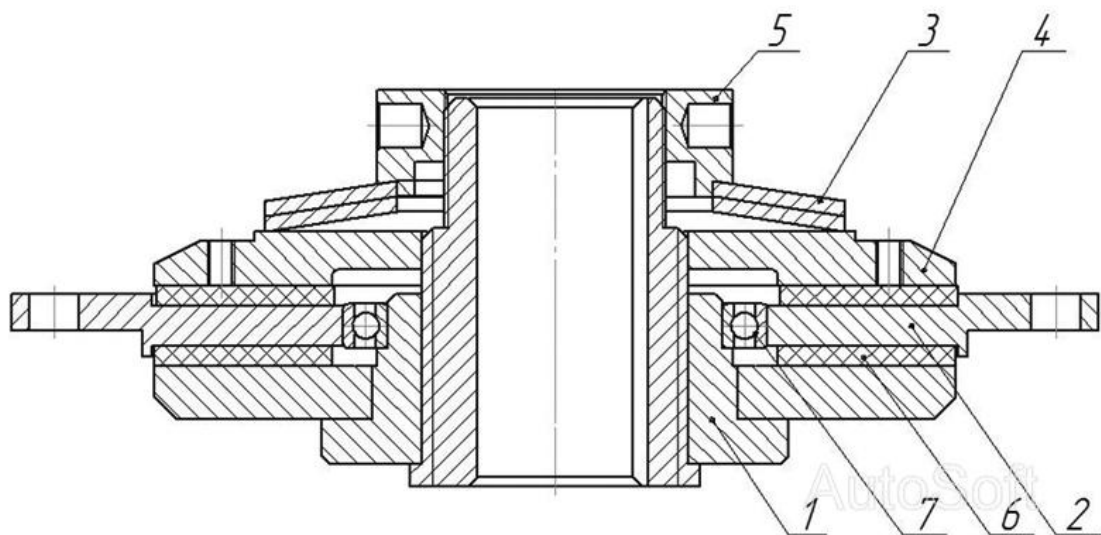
Конструкція запобіжної муфти: 1 – напівмуфта, 2 – диск, 3 – пружина, 4 – диск, 5- гайка, 6 - накладка фрикційна, 7 - підшипник
